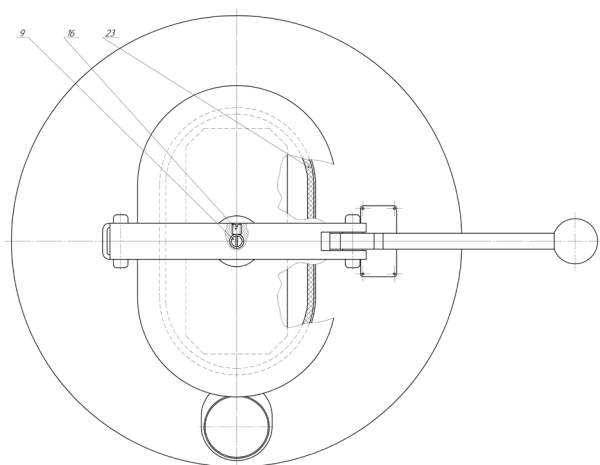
Загальний вигляд пристрою CARBOFit-400 (вигляд зверху)
